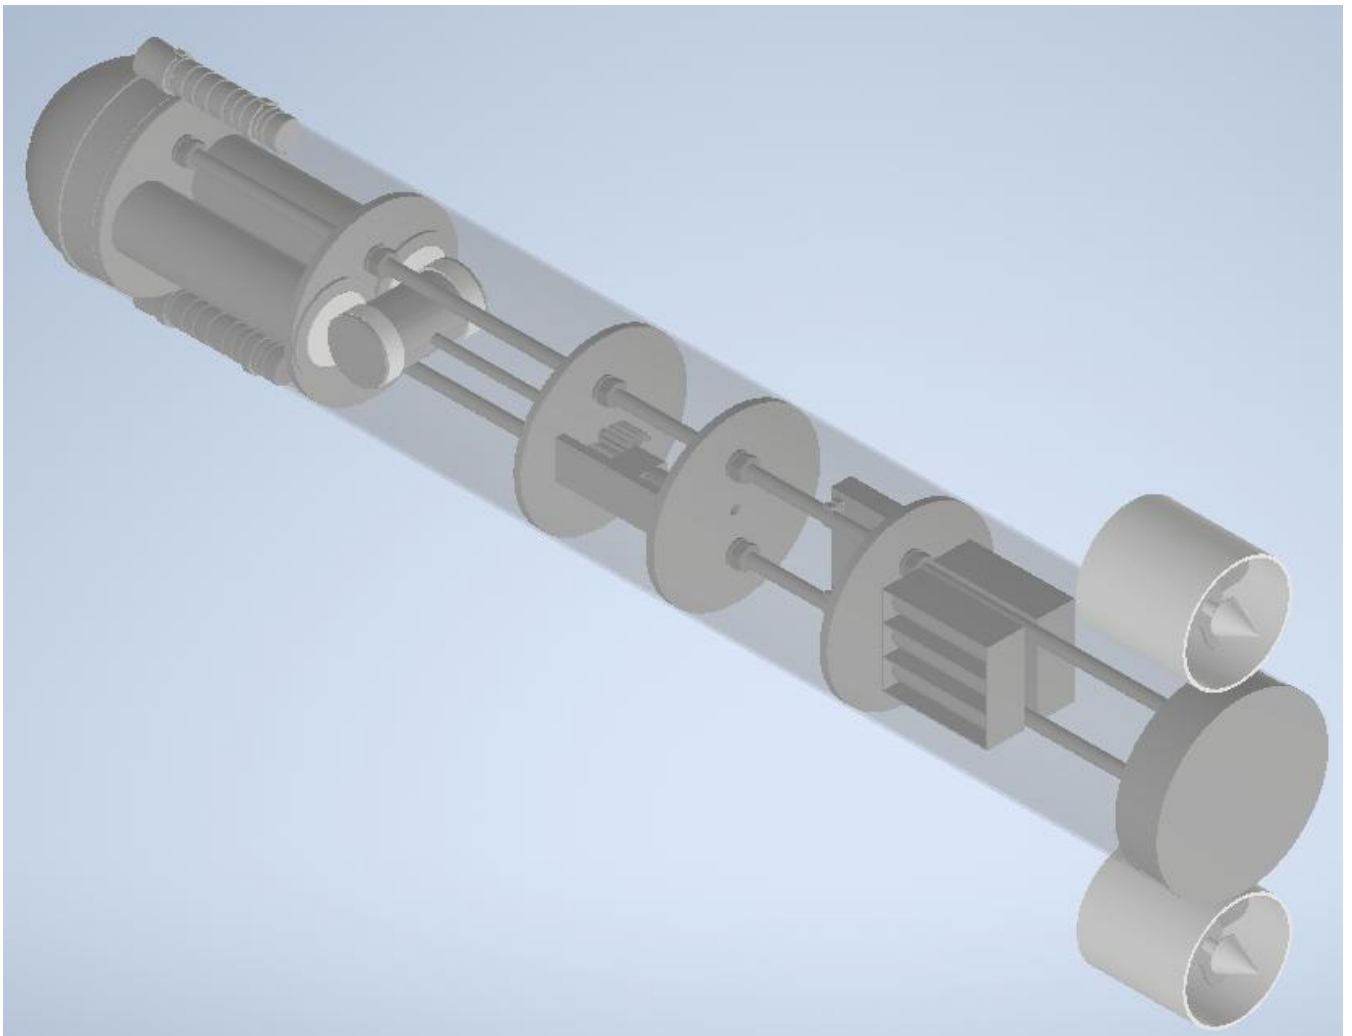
Початкова версія дрона з двома гвинтами та довгим корпусом
